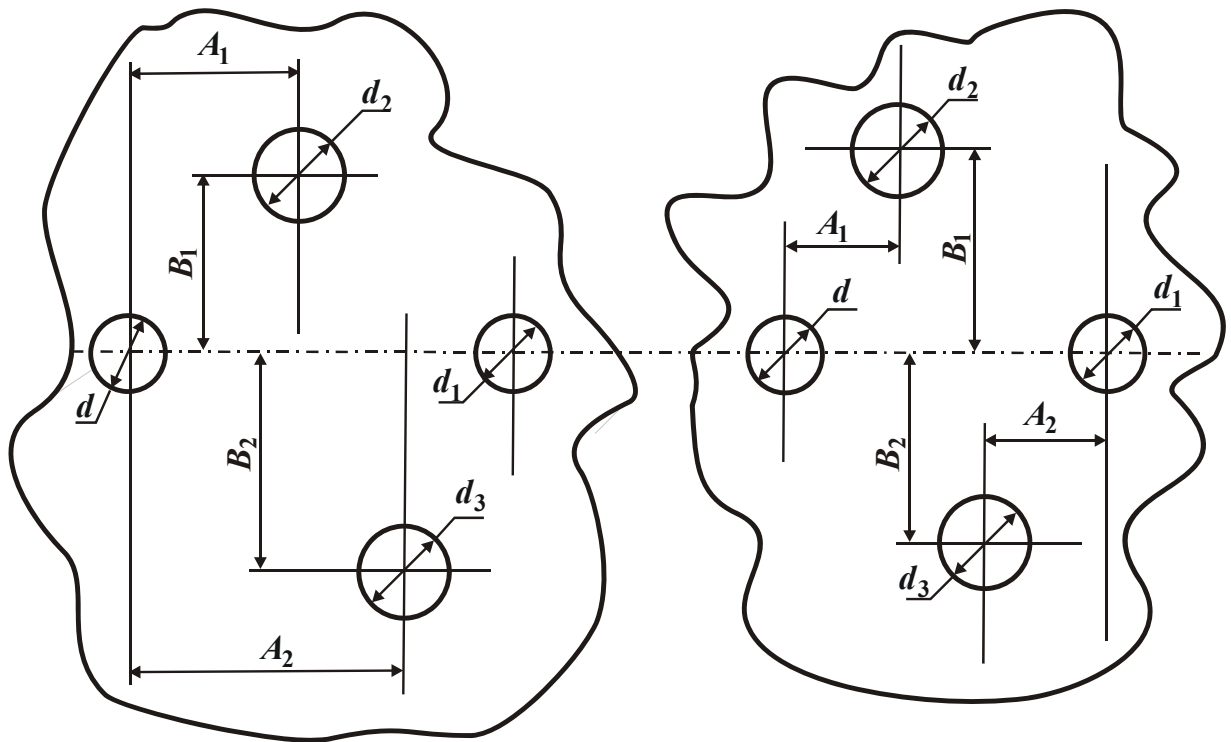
Варианты установки корпусной детали по двум цилиндрическим отверстиям.
